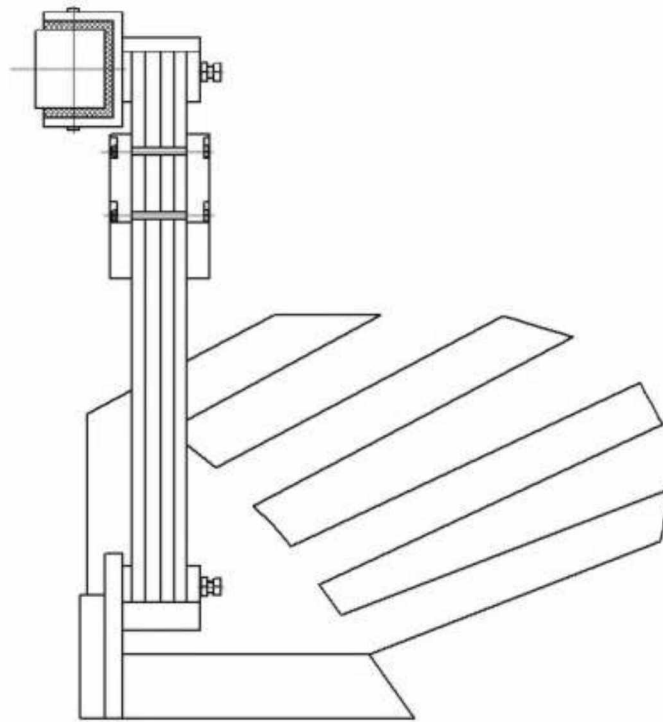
Схема корпусу плуга з вібруючою стойкою (вид ззаду)
